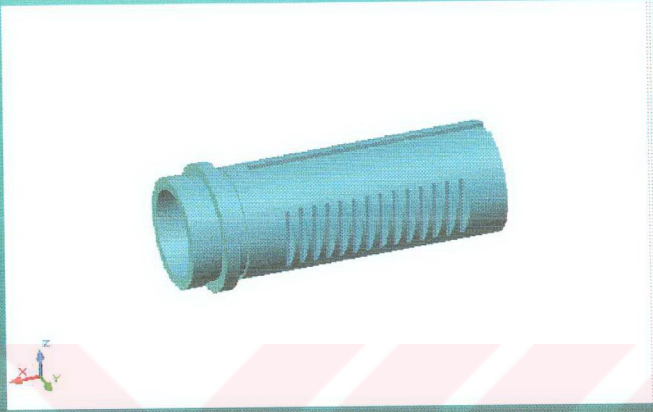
Motor mili ve iş mili göbek kasnağı-3D
